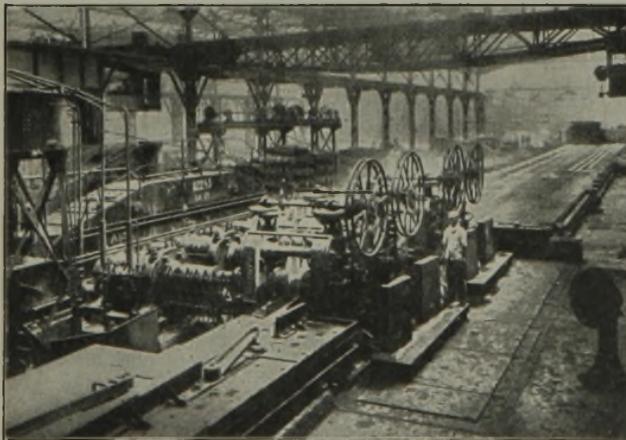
Kontinuierliche Fertigstraße mit Gerüsten.
